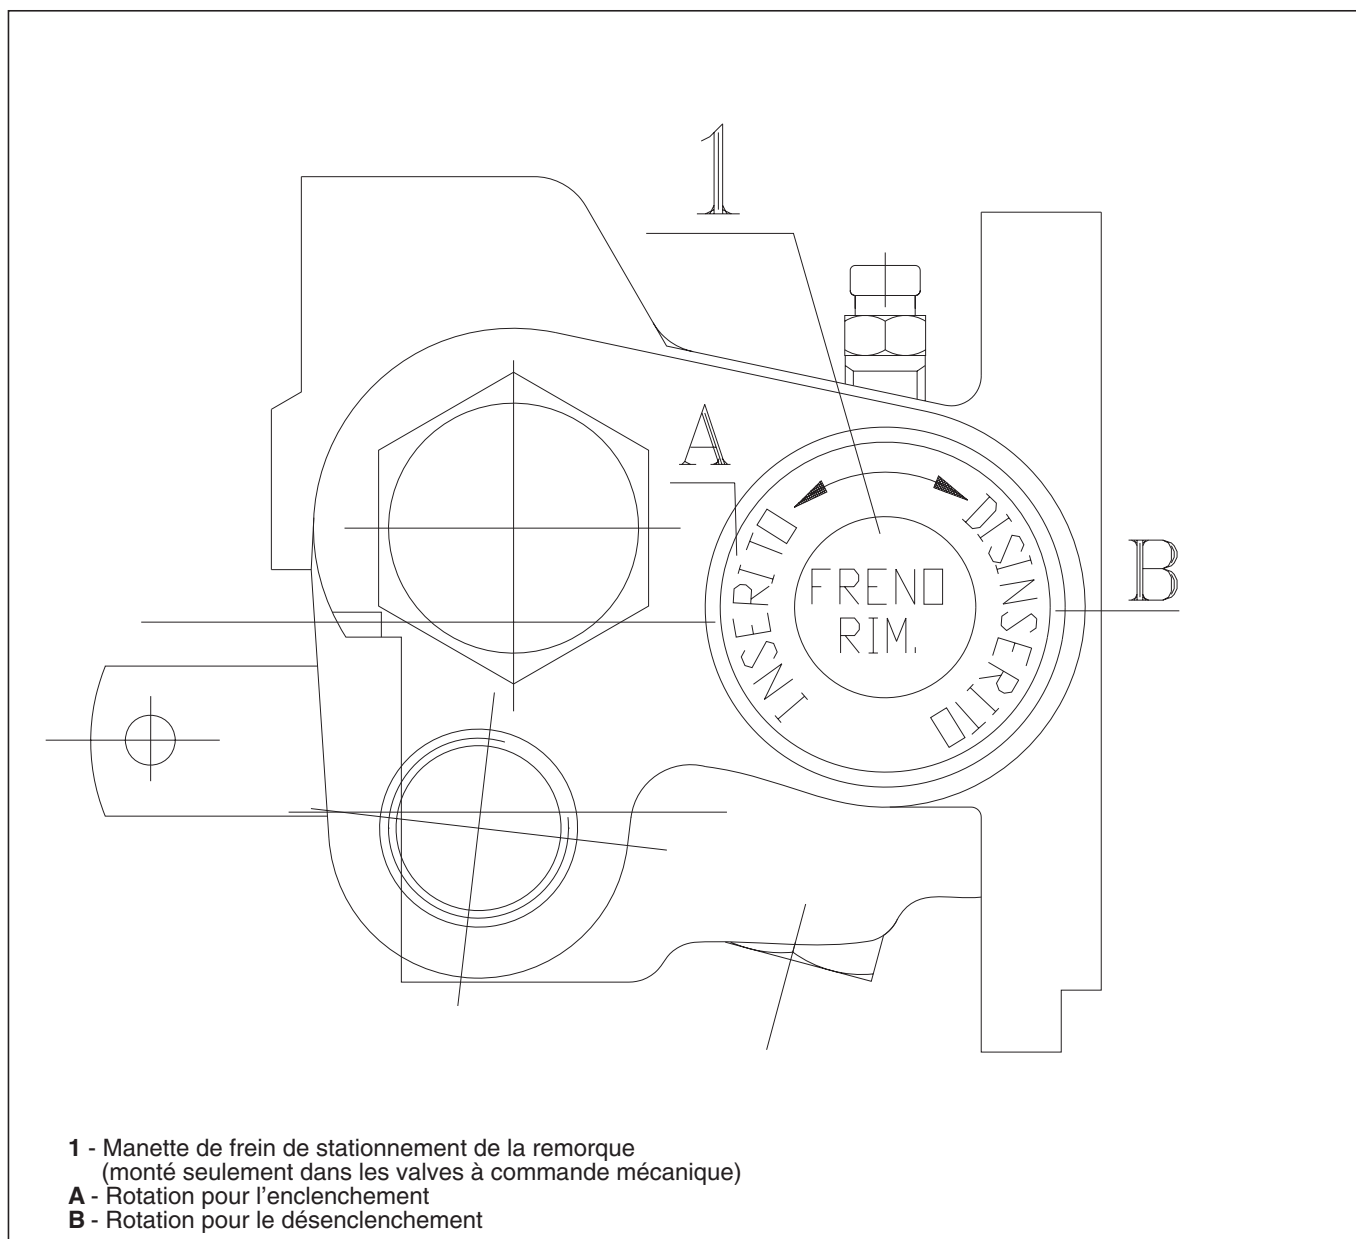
Bloc distributeur pour le freinage hydraulique de remorque.
